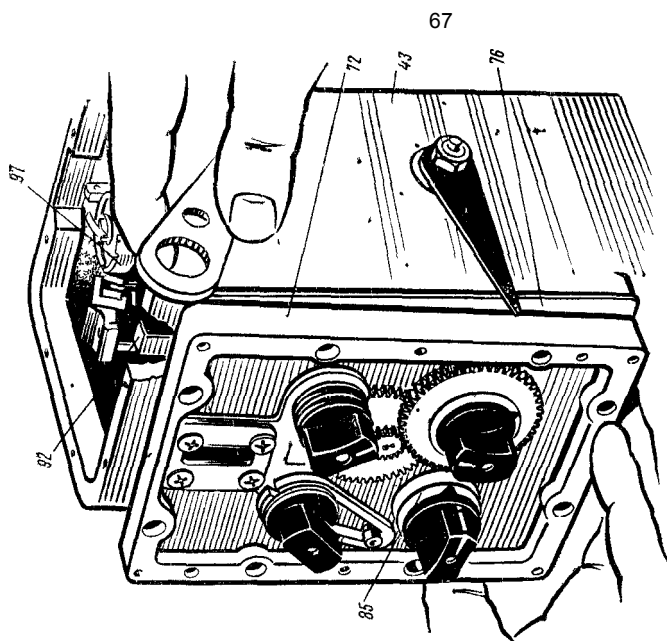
43 — корпус регулятора, 72 — панель, 76 — прокладка панели, 85 — указатель нагрузки, 92 — планка ограничителя нагрузки, 97 — рычаг регулирования неравномерности
